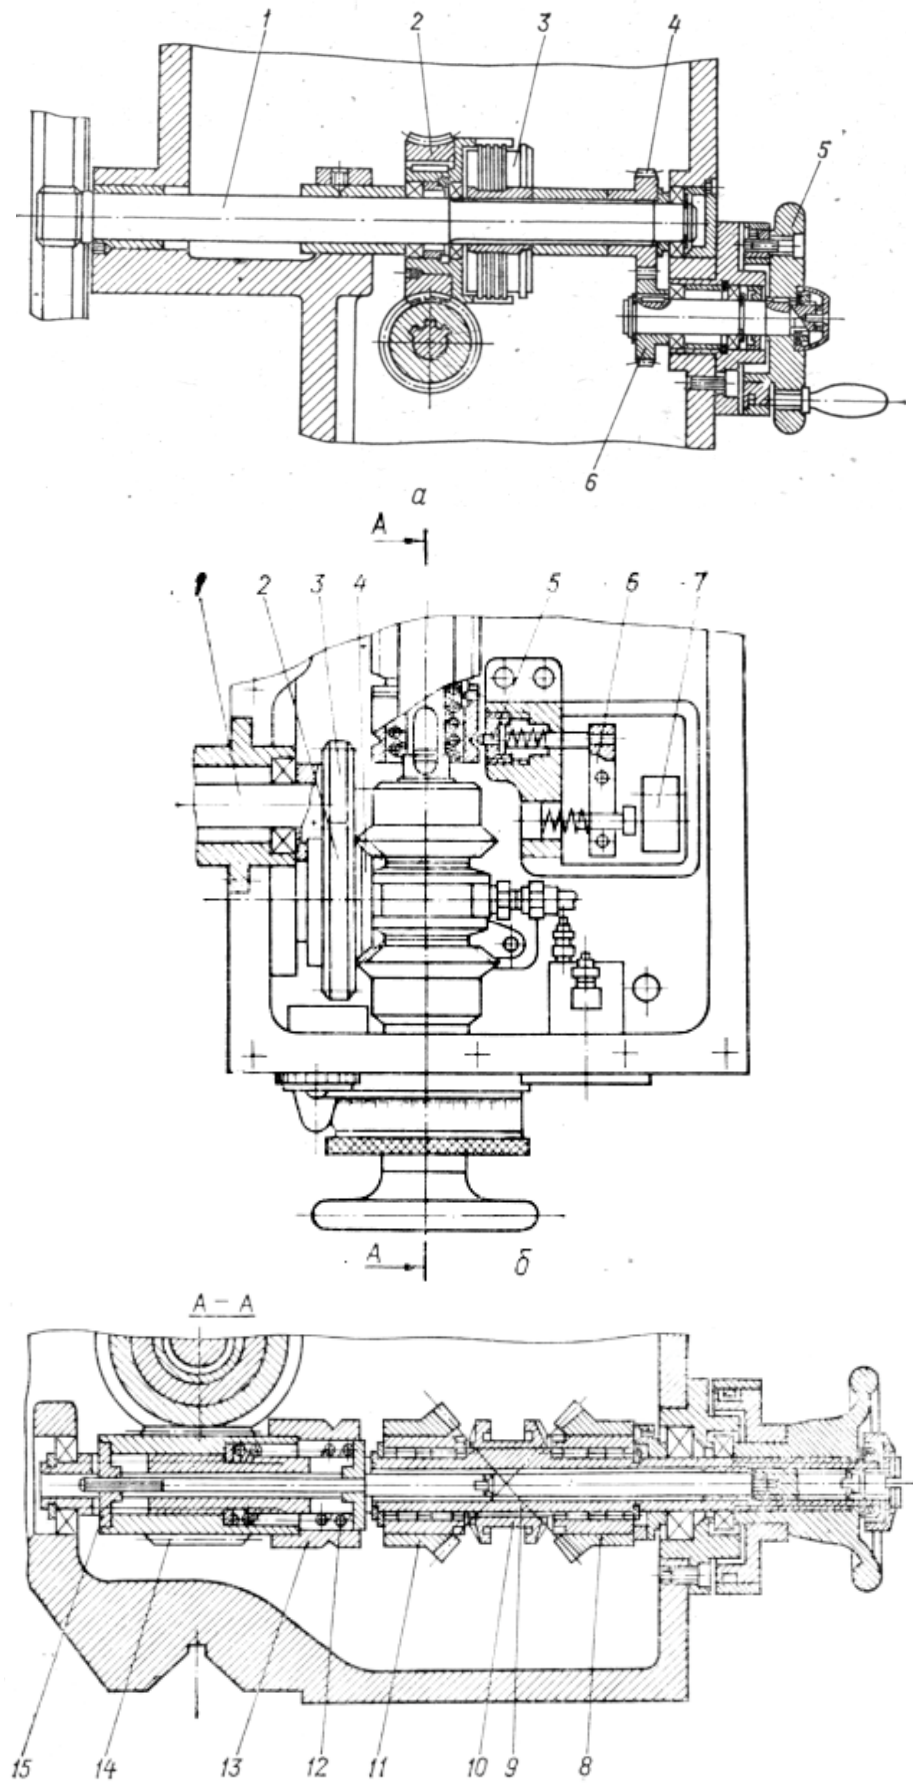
Приводи ручного обертання (а) та автоматичної кругової подачі (б) револьверної головки верстата мод. 1Г340П
